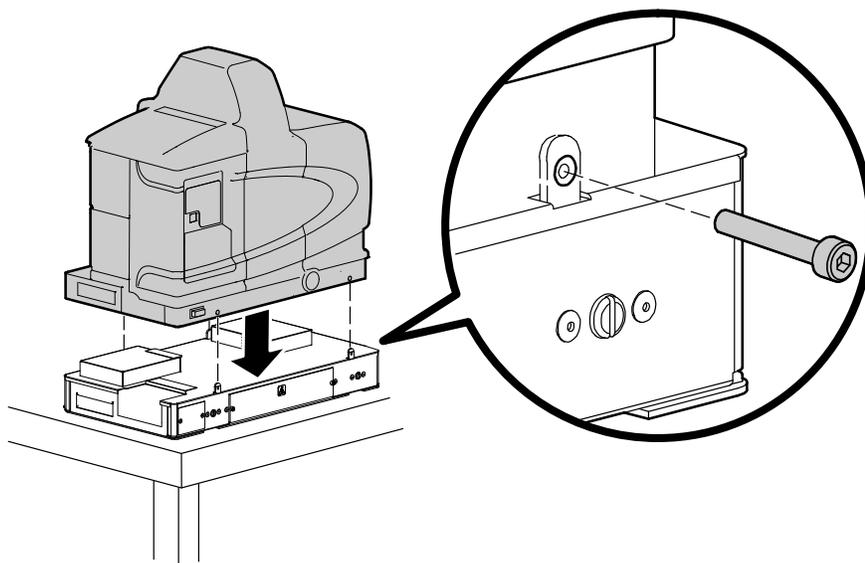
Montaggio dell'unità di fusione sul trasformatore
